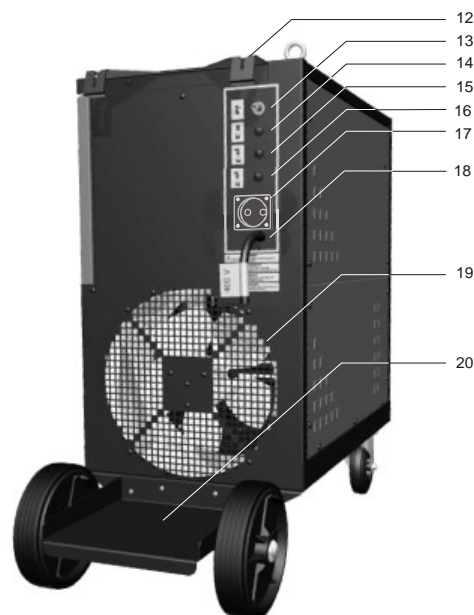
Внешний вид сварочного полуавтомата – Задняя панель
